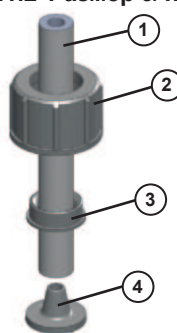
Зажимное соединение для шланга 6/12 (внутренний и наружный диаметр в мм)
